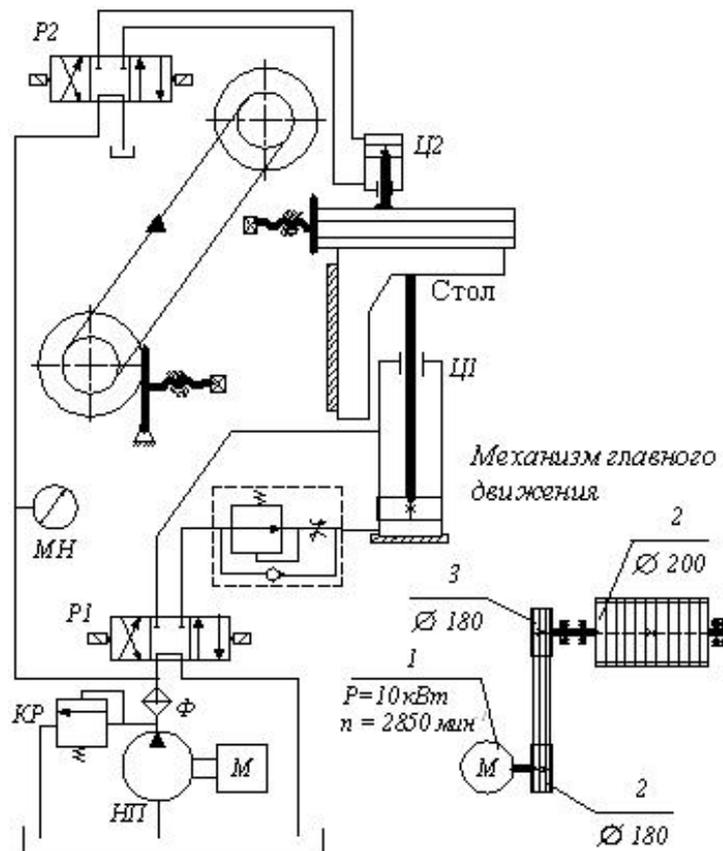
Гидрокинематическая схема шипорезного станка ШПК40
